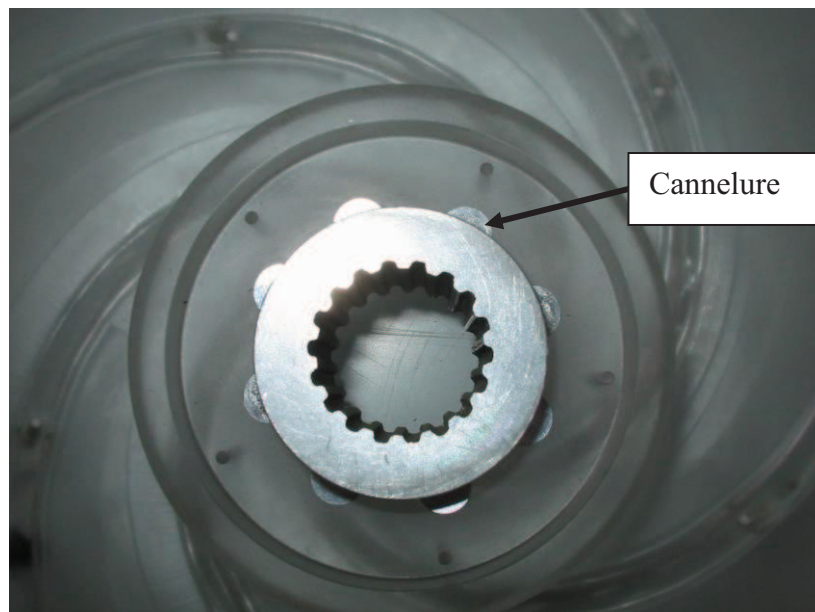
Photographie du moyeu de la roue en PMMA (vue de derrière)
